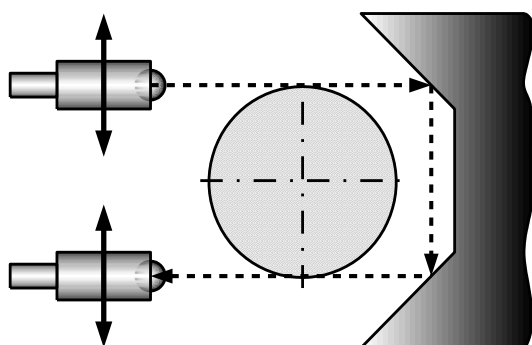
Тіньовий двобічний лазерний вимірювальний пристрій
